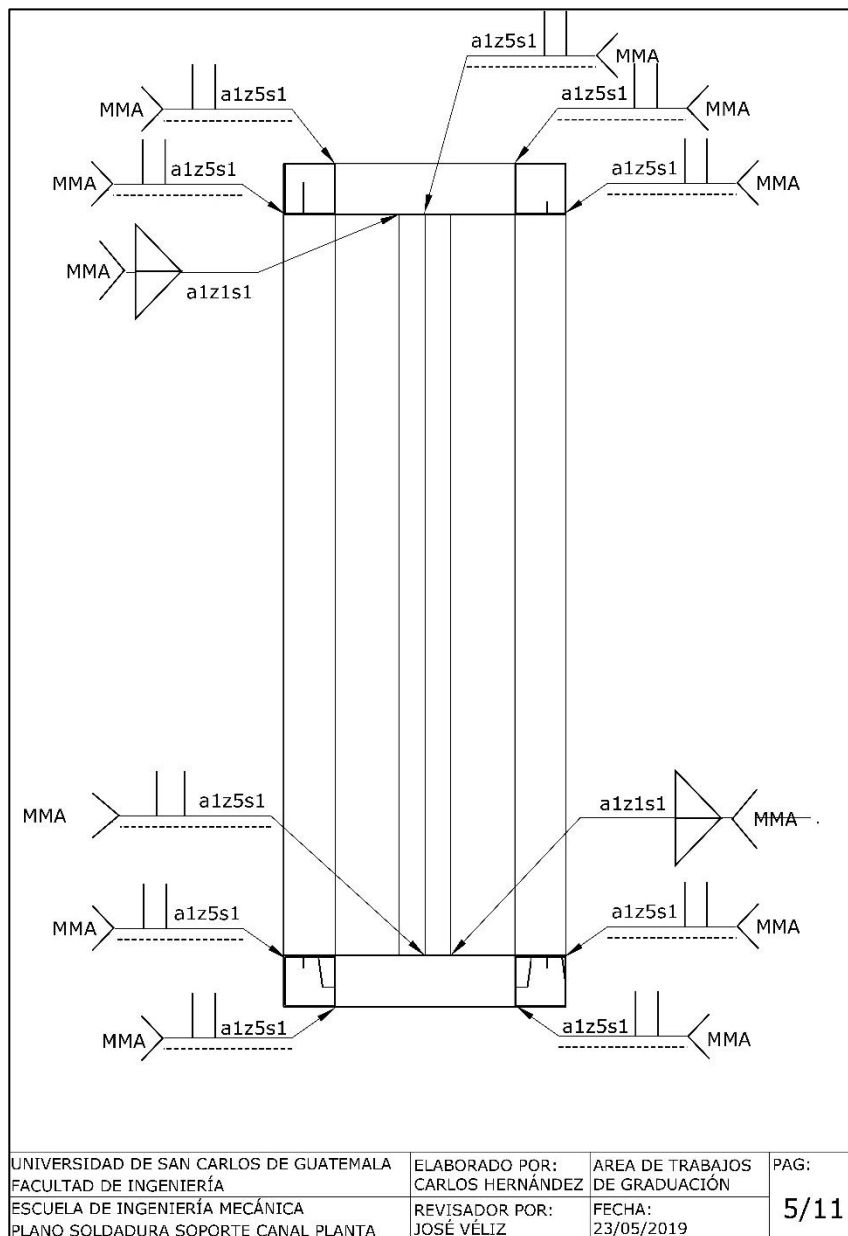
Plano de soldadura de soporte del canal vista frontal
